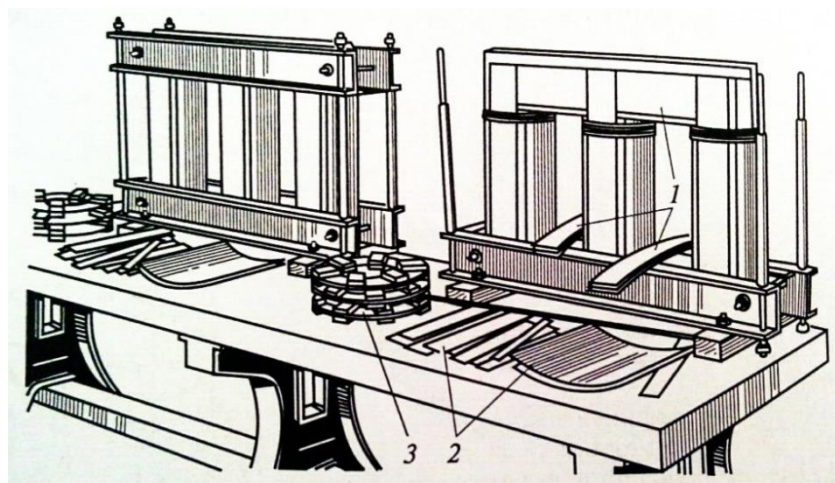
Расшихтовка верхнего ярма трансформатора мощностью 100 кВА: 1 — пластины ярма; 2 — детали, подготовленные к сборке; 3 — ярмовая изоляция
